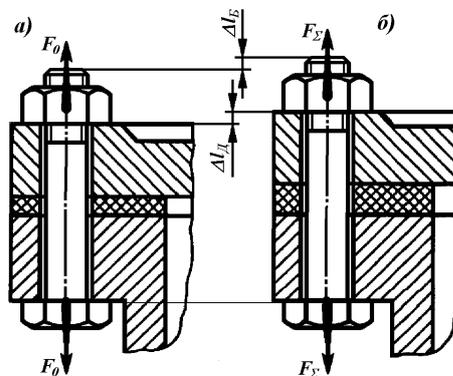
Болтовое соединение корпуса и крышки ресивера
